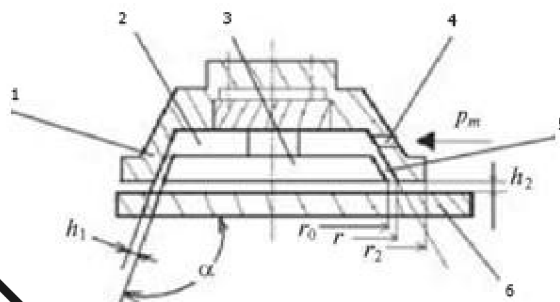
Струменєво-вакуумний захоплювальний пристрій:
